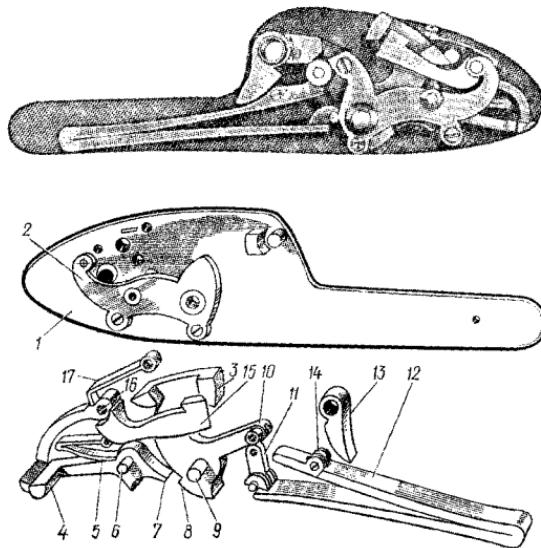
Замок ружья МЦ11 (типа Дж. Пердея) и его устройство: 1—замочная доска (металлическая пластина); 2—накладка; 3—курок; 4—спусковой рычаг; 5—пружина спускового рычага; 6—ось спускового рычага; 7—шептало; 8—боевой взвод курка; 9—ось курка; 10—рычажной выступ курка; 11—цепочка; 12—боевая пружина; 13—серьга нагнетания боевой пружины; 14—ролик боевой пружины; 15—интэрсептор (перехватыватель) курка; 16—отверстие оси интэрсептора; 17—пружина интэрсептора.
